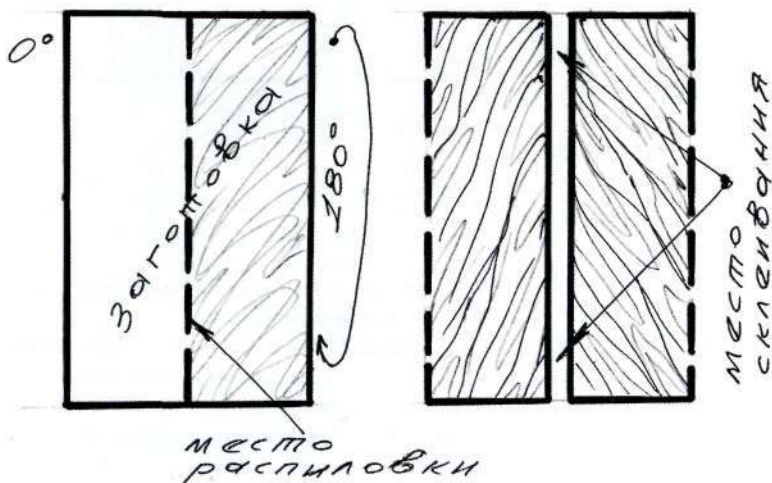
Схема раскладки дерева при работе над ножами (вид с торца заготовок)
